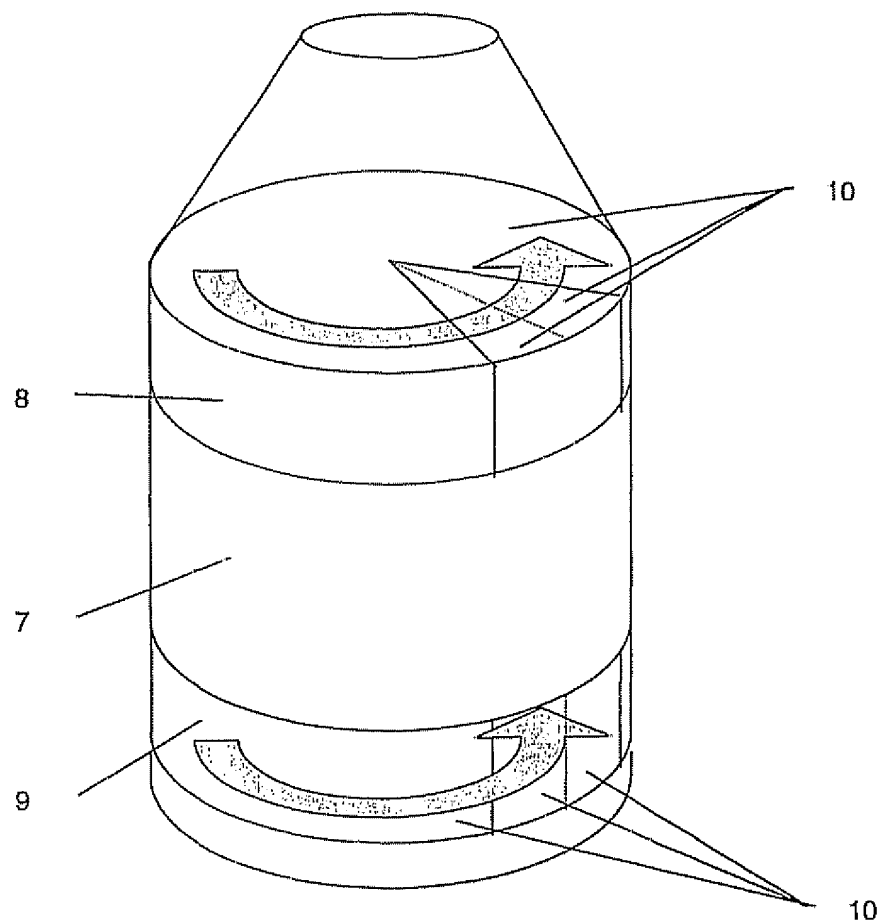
Beispielhafte Ausführung einer Statorausführung mit segmentweiser Anströmung und Drehrichtung.
